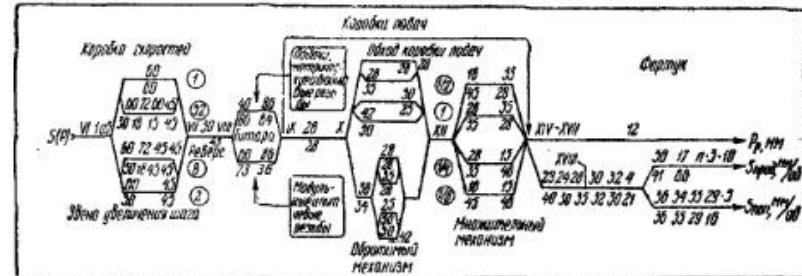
Структурная формула привода подачи суппорта станка 16К20
